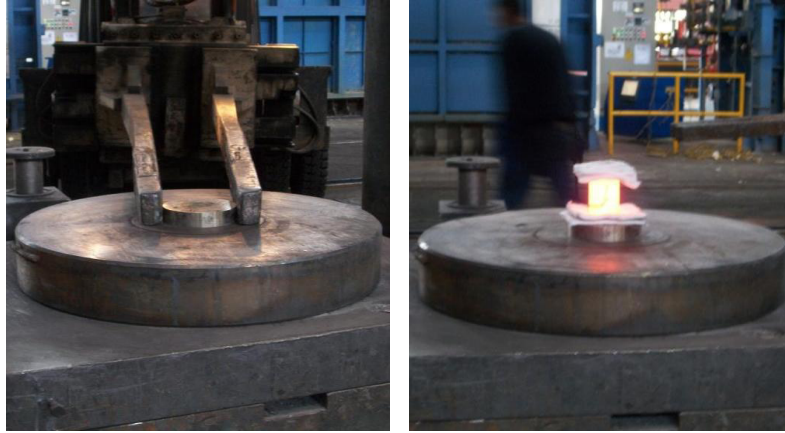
Ajuste y aislamiento de los cilindros en las prensas en planta
